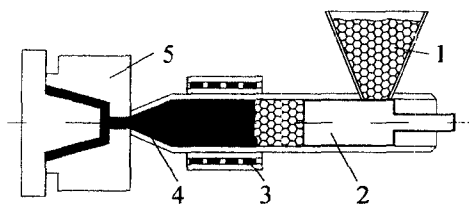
Схема изготовления изделий из пластмасс методом литья под давлением
